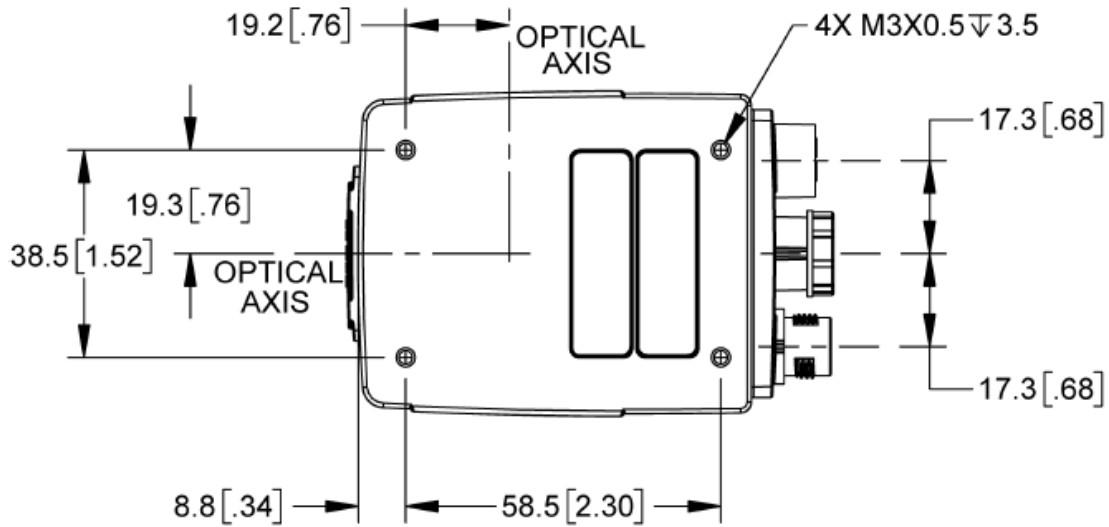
Dimensiones del reverso de la cámara IS7802. [28]
